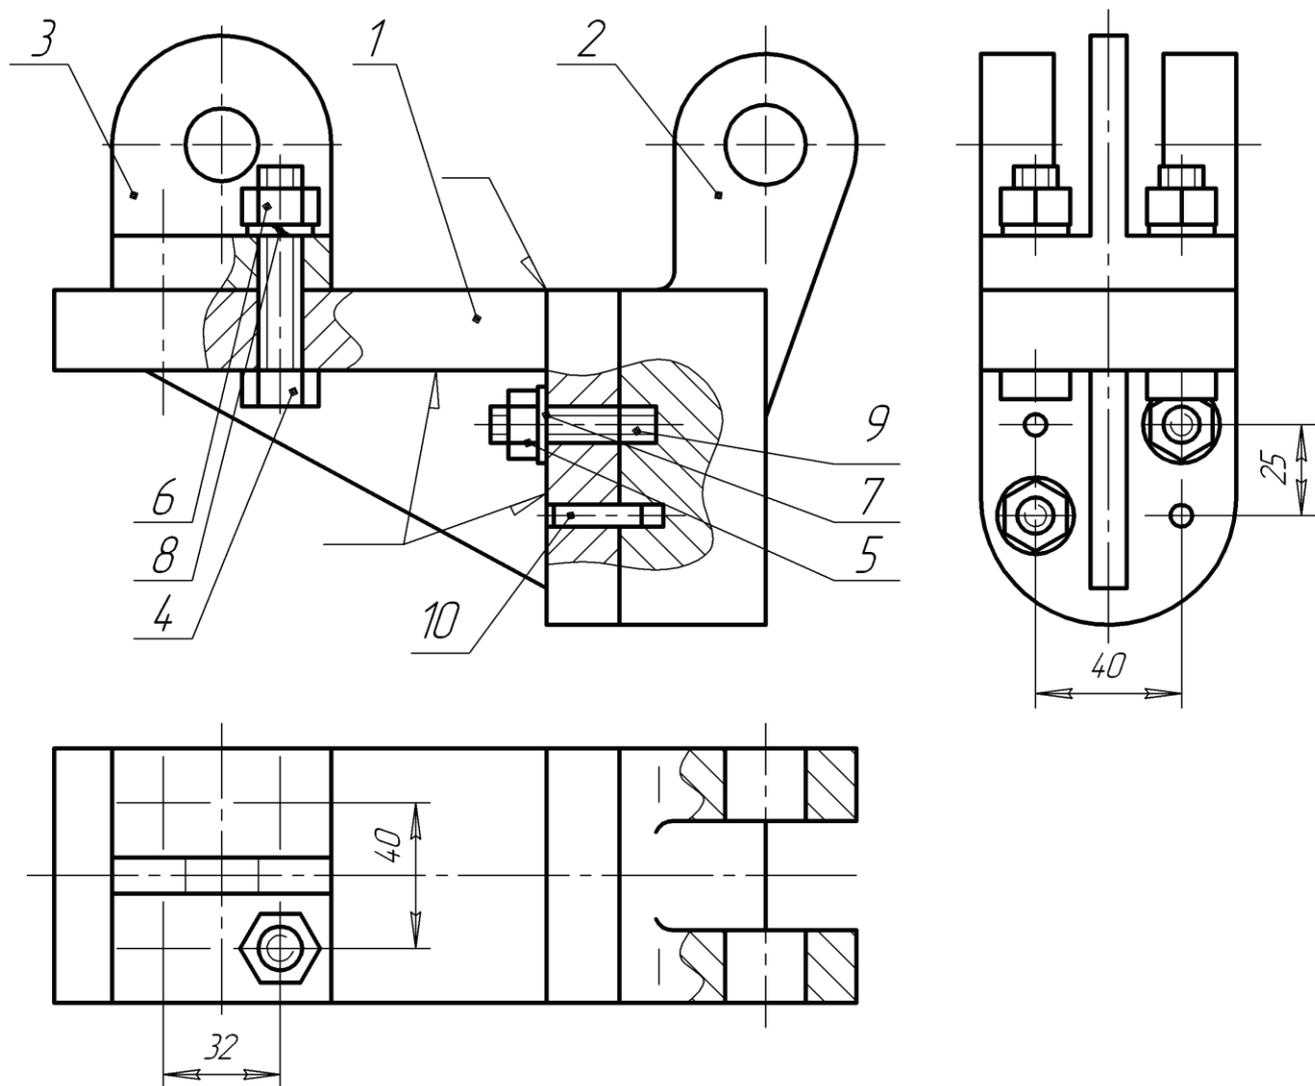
Сборочный чертеж изделия «Кронштейн»
